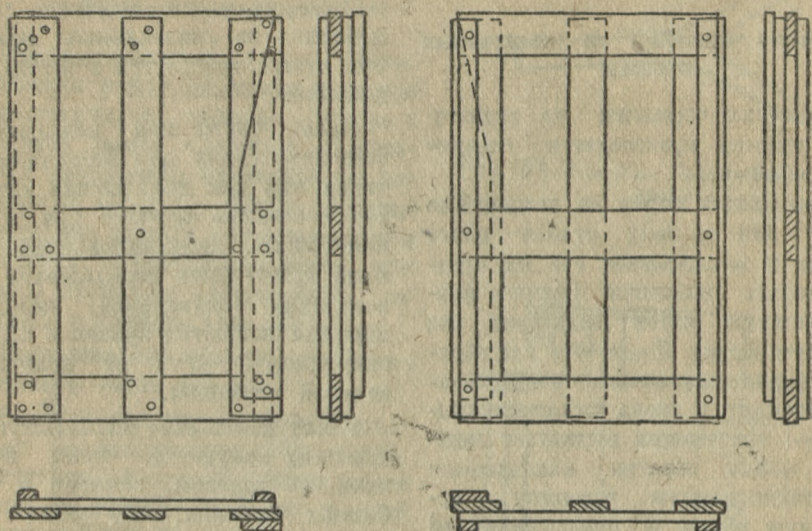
Рамка для сушки пазовой прессованной черепицы
